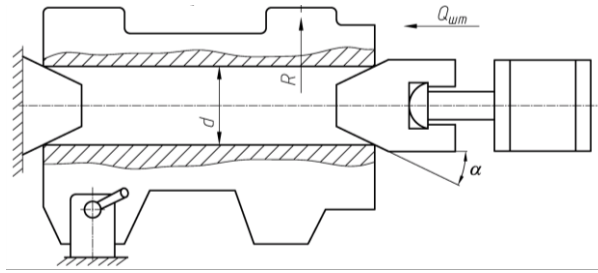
Принципова схема привода пристрою фрезерування
